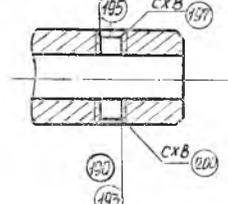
Фрагменты чертежа комплексного представителя группы деталей 001 «Вилки и ушковые болты»
